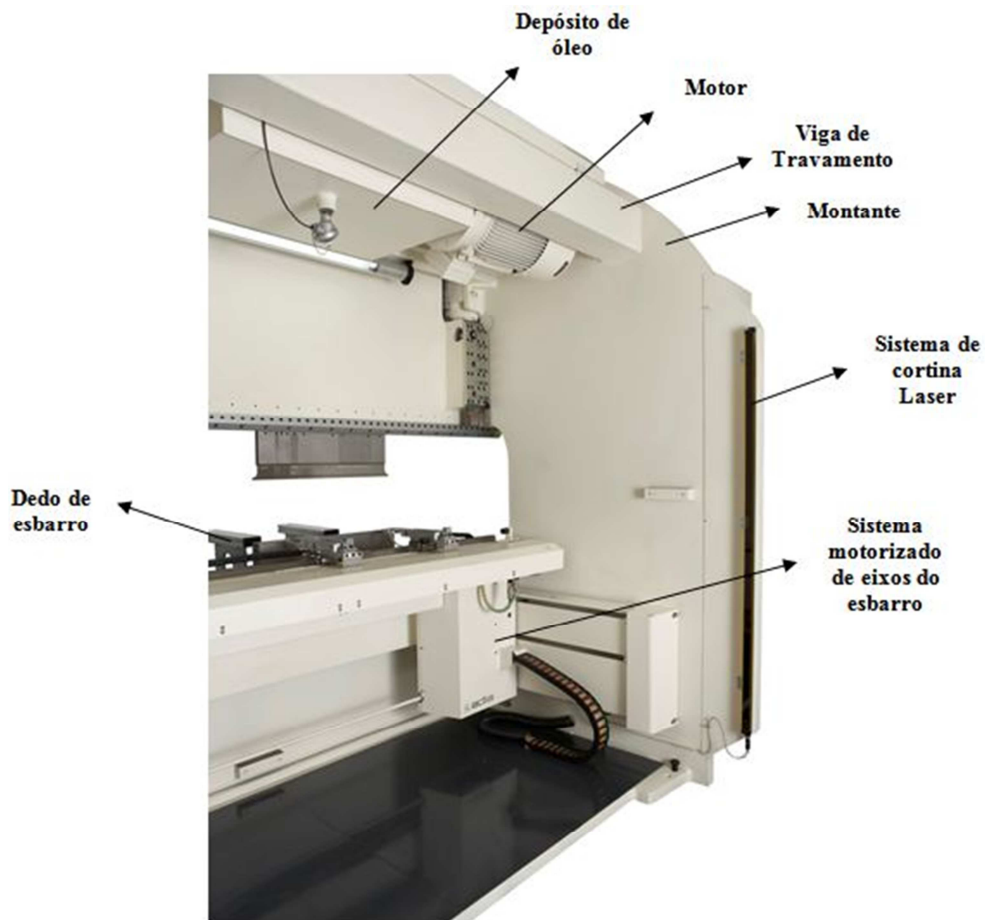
Componentes de uma quinadora (vista traseira)
